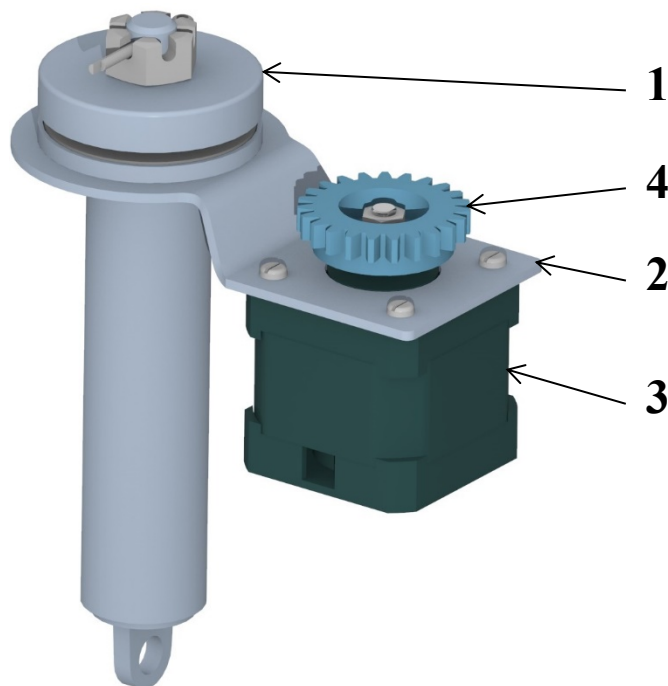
Detailní pohled na ozubené kolo
